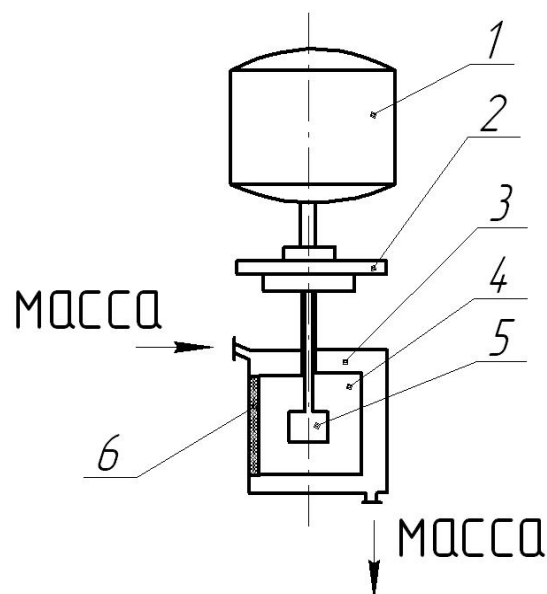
Схема виброинерционной мельницы: 1 – электродвигатель; 2 – гибкая муфта; 3 – корпус цилиндрический; 4 – ротор; 5 – дисбаланс; 6 – слой сжатых волокон
